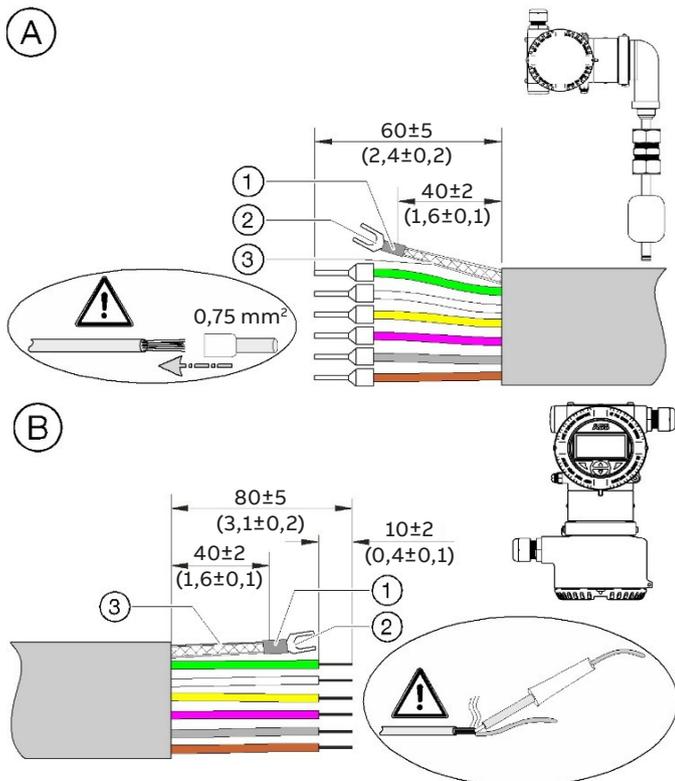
Dimensões do cabo de sinal em mm (polegadas)
